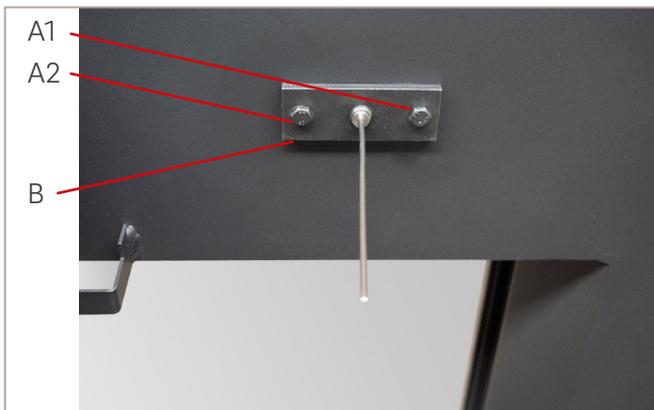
SMR-Feuerraumfühler an Rückwand befestigt
